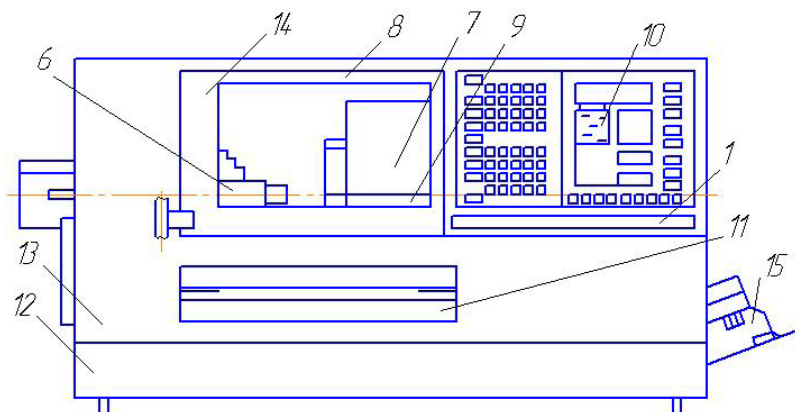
Элементы станка: вид спереди: 6 – шпиндель, 7 – поворотное устройство, 8 – светильник, 9 – задняя бабка, 10 – клавиатура, 11 – подставка станка, 12 – дверь, 13 – насос
